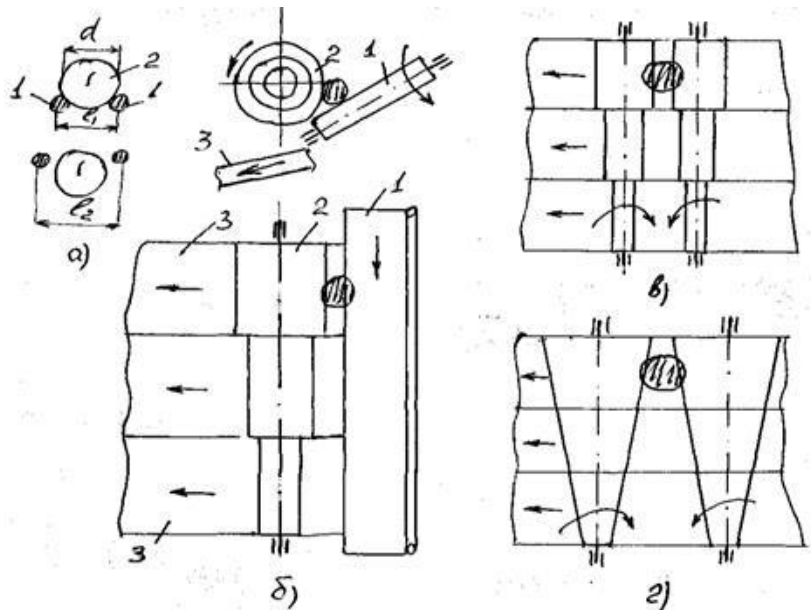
Схеми пристроїв для калібрування: а) тросове б) валково-стрічкове; в) з ступінчастими валами г) з валами (шнеками) змінних діаметрів.
